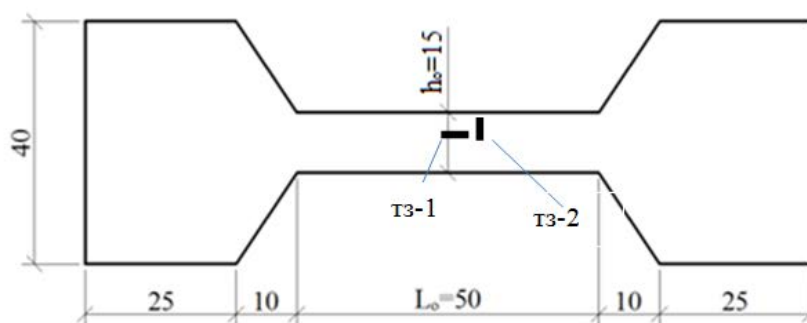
Образец-лопатка для испытаний на растяжение, размеры в мм.
